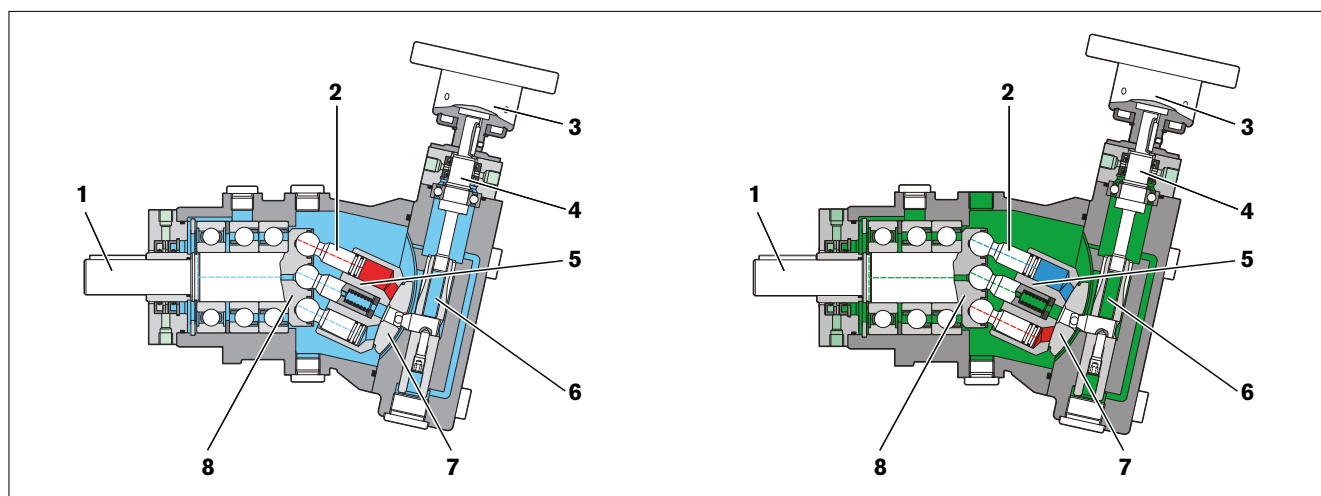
Aufbau der A7VK Baureihe 10, linke Darstellung – offene Bauart, rechte Darstellung – geschlossene Bauart
